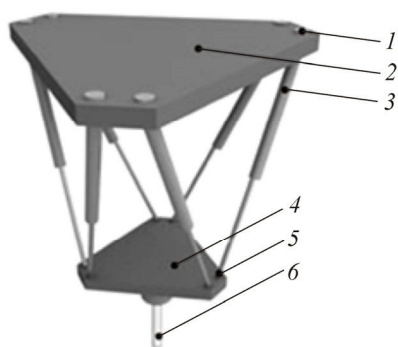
Кинематическая схема измерительной машины: 1 – шарниры; 2 – неподвижная рама; 3 – стержни переменной длины; 4 – каретка; 5 – шарниры; 6 – инструмент
